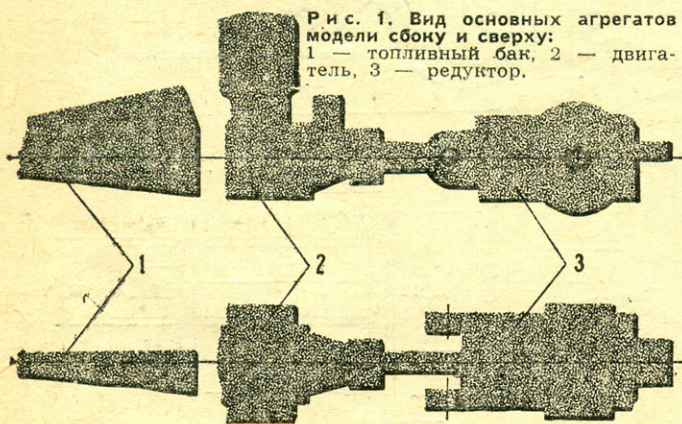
Вид основных агрегатов модели сбоку и сверху: 1 — топливный бак, 2 — двигатель, 3 — редуктор.
